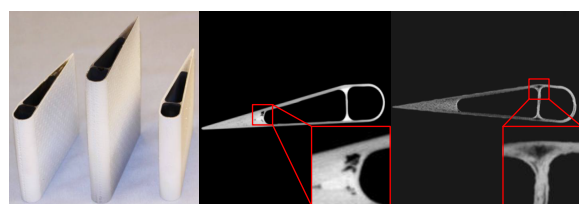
CT 对异形材料样件进行检测^[72]Fig. 16 CT inspection of irregularly shaped material samples^[72]
